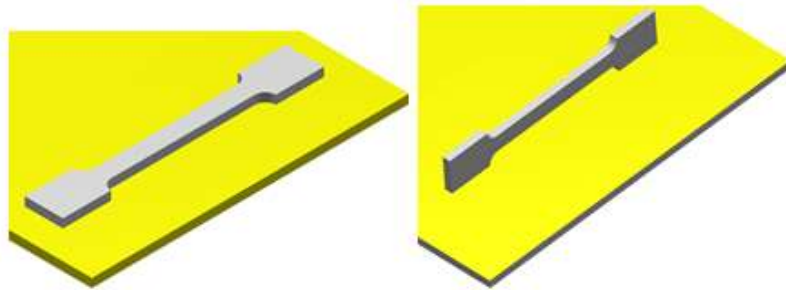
Posición de impresión de probetas, Fuente: Propia
